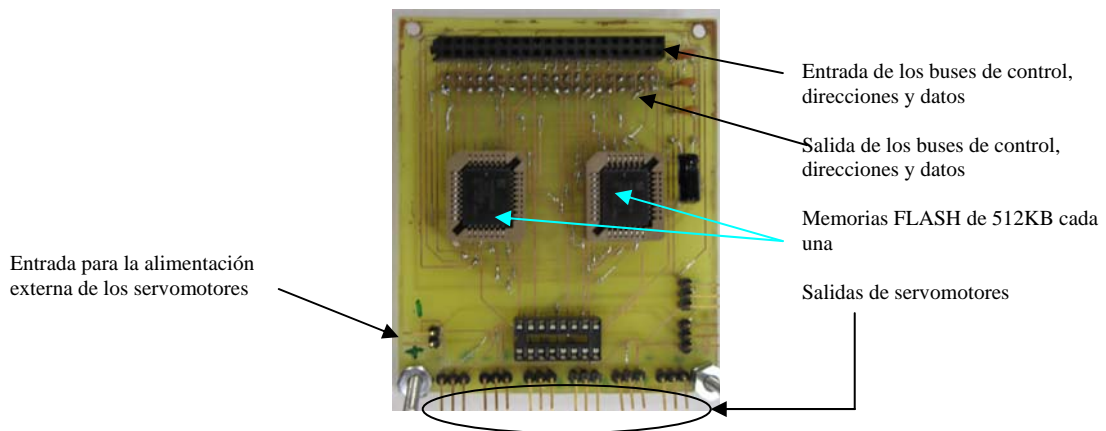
Ensamble físico de la segunda parte de la tarjeta de control.
